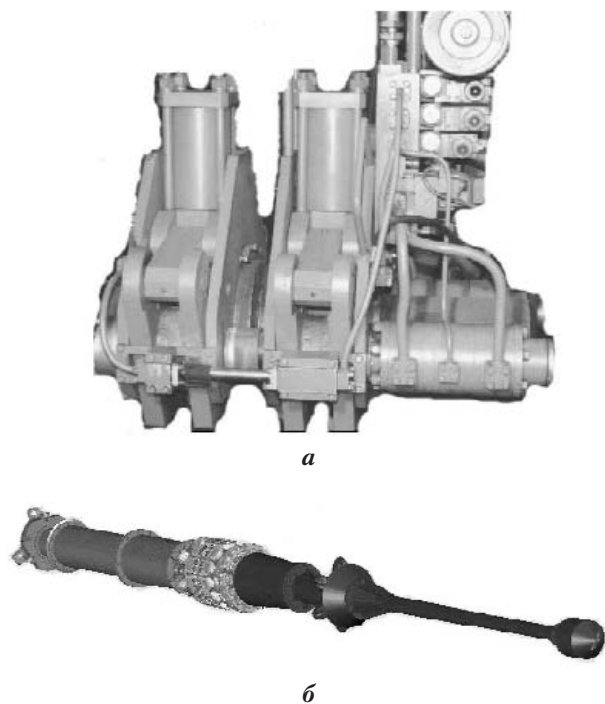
Новое поколение оборудования для контактно-стыковой сварки трубопроводов: *а* – машина для сварки трубопроводов  $\varnothing$  114–219 мм (вес 2 т, мощность 100 кВА); *б* – внутритрубная машина К1006 для сварки труб  $\varnothing$  1420 мм с толщиной стенки 22 мм (вес 16 т, мощность 600 кВА)
